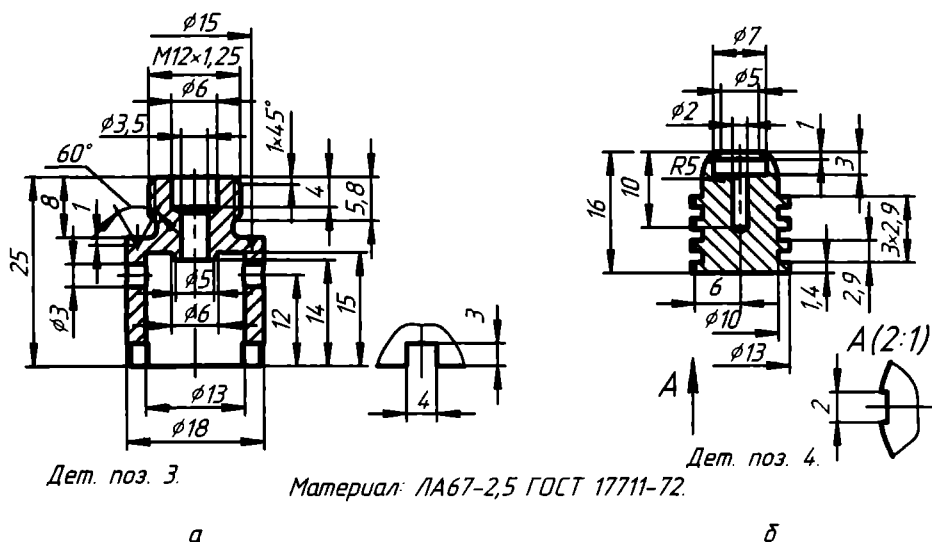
Чертежи: а — цилиндра; б — поршня
